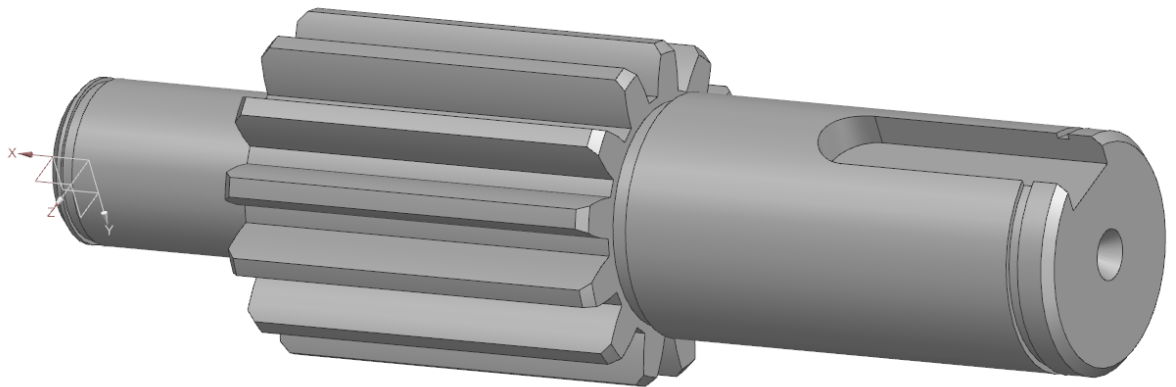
3д модель деталі «Вал-шестерня» після обробки
